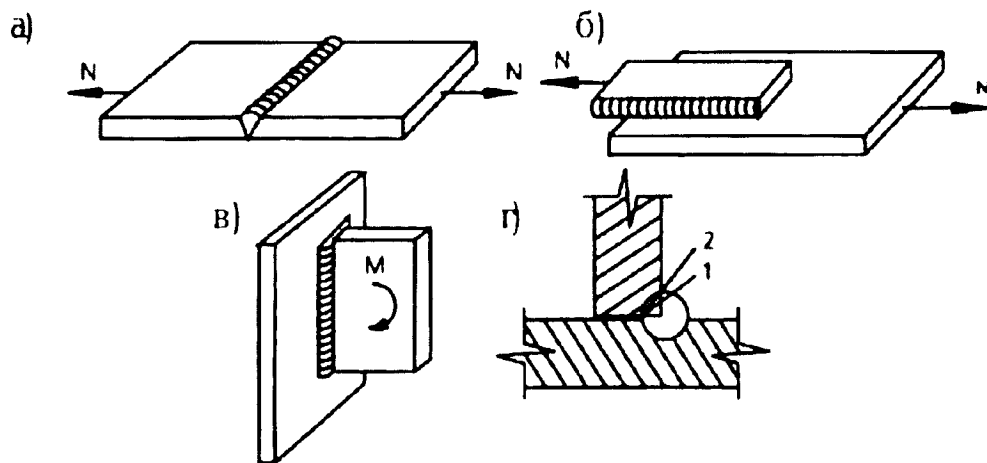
Сварные соединения элементов металлических конструкций: а - стыковой шов, б, в - фланцевый угловой шов; г - схема расчетных сечений (1 - сечение по металлу шва; 2 - сечение по металлу границы сплавления)
